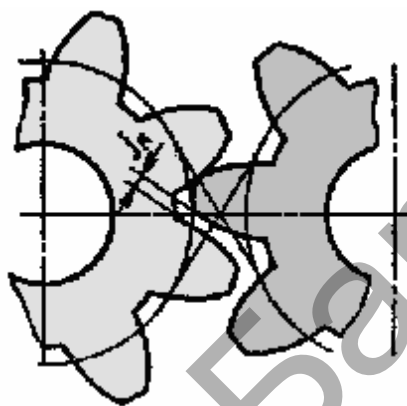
Боковой зазор в зубчатой передаче
